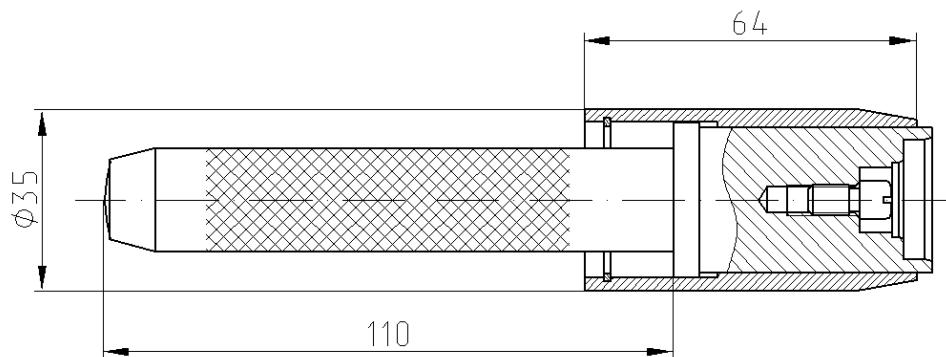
ЗМ 7853-4355, Оправка для напрессовки
